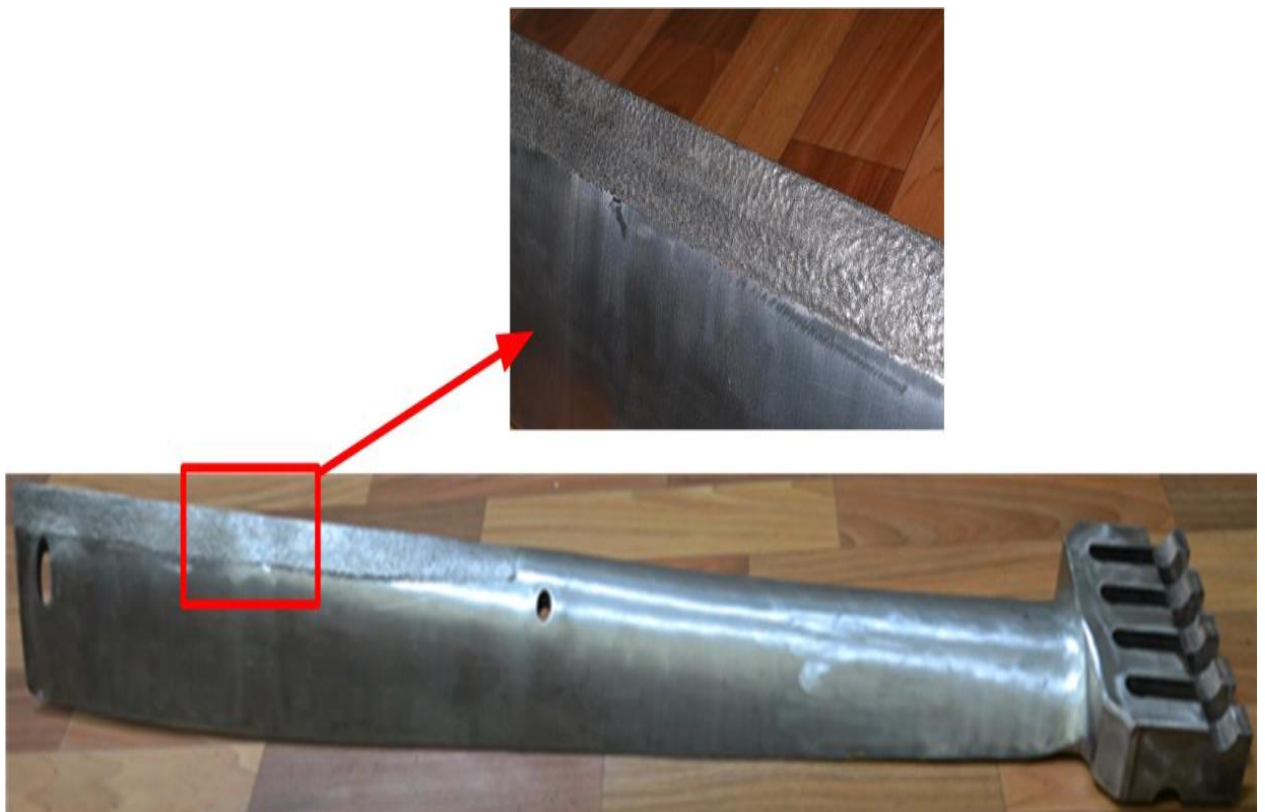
Внешний вид рабочей лопатки последней ступени паровой турбины с ЭИЛ со стеллитовым покрытием на входной кромке
